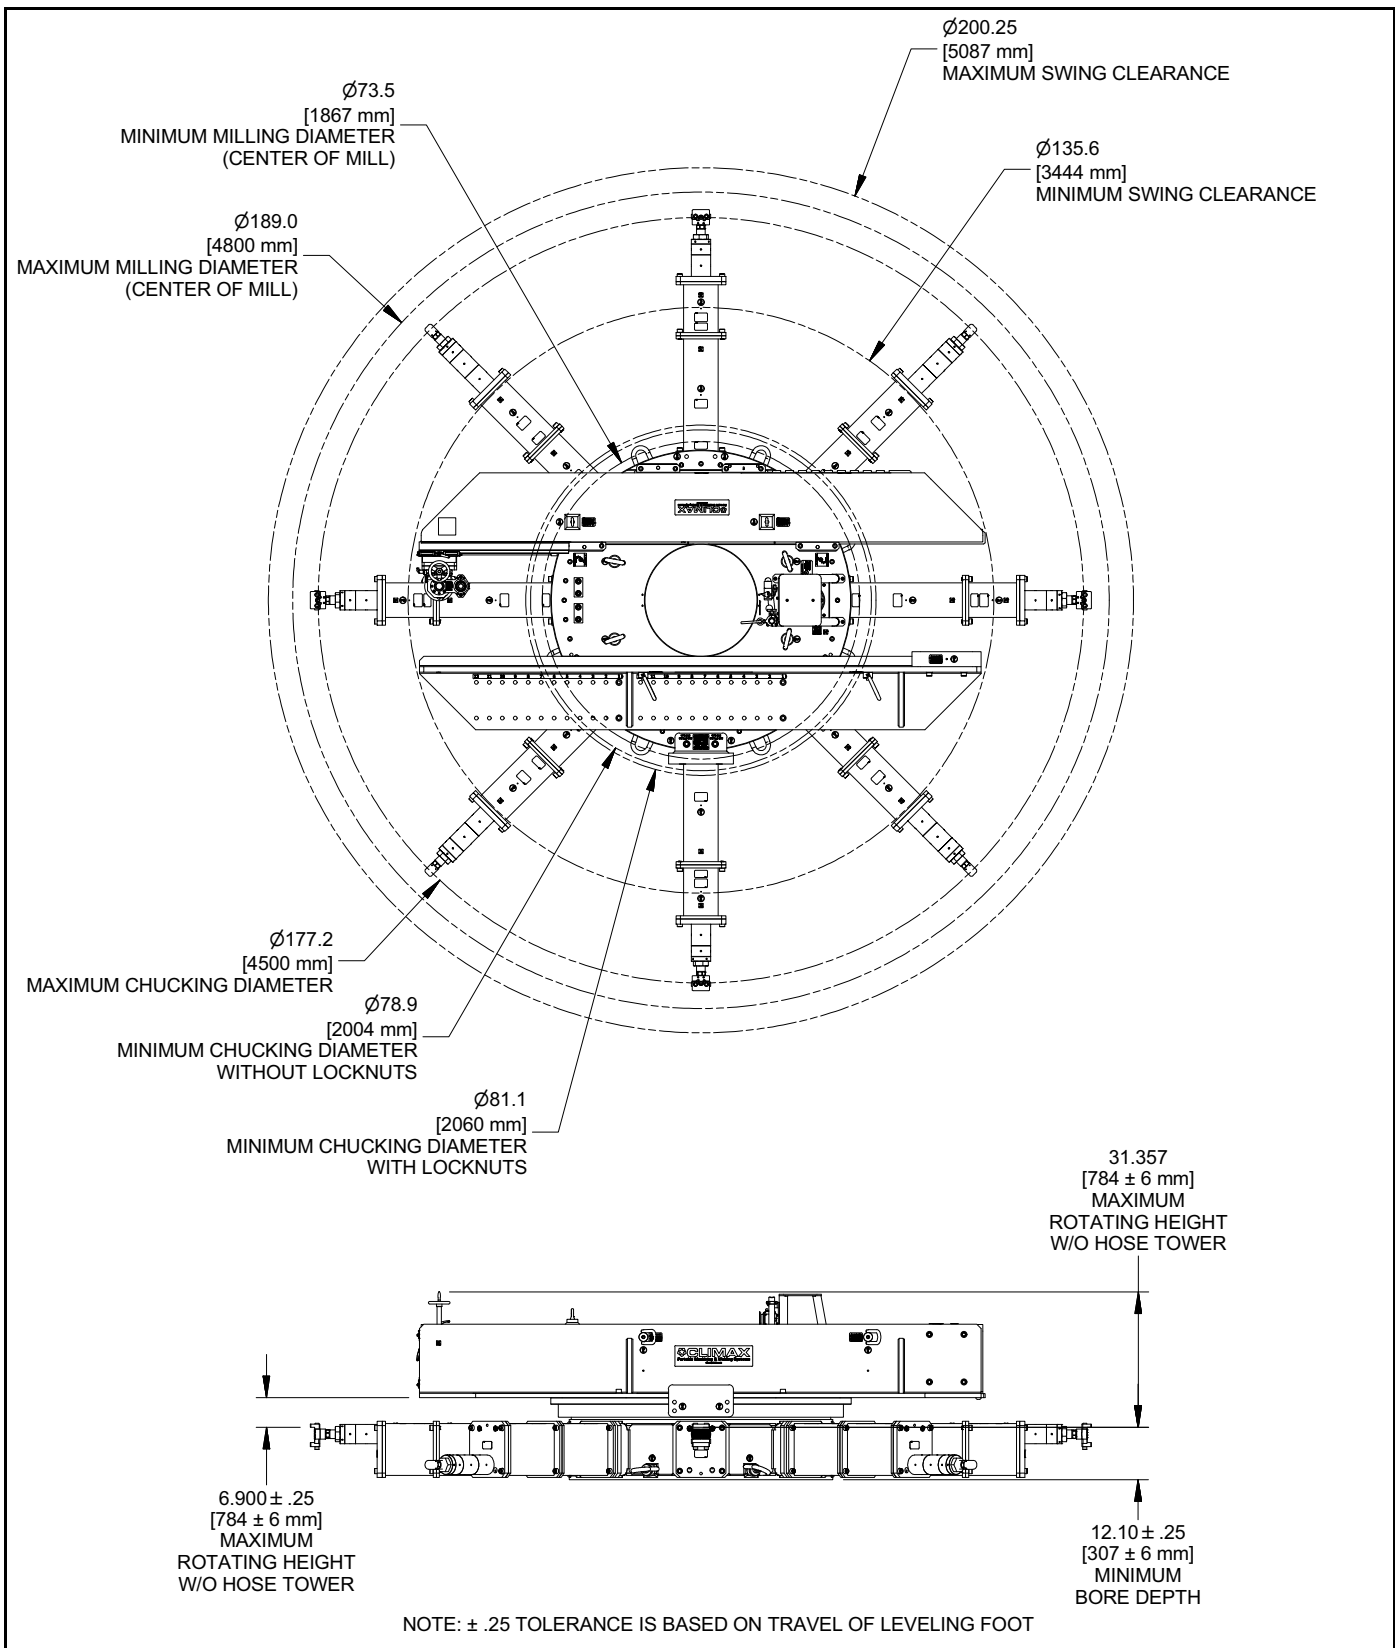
DIMENSIONS DE LA MACHINE À MONTAGE SUR DI
